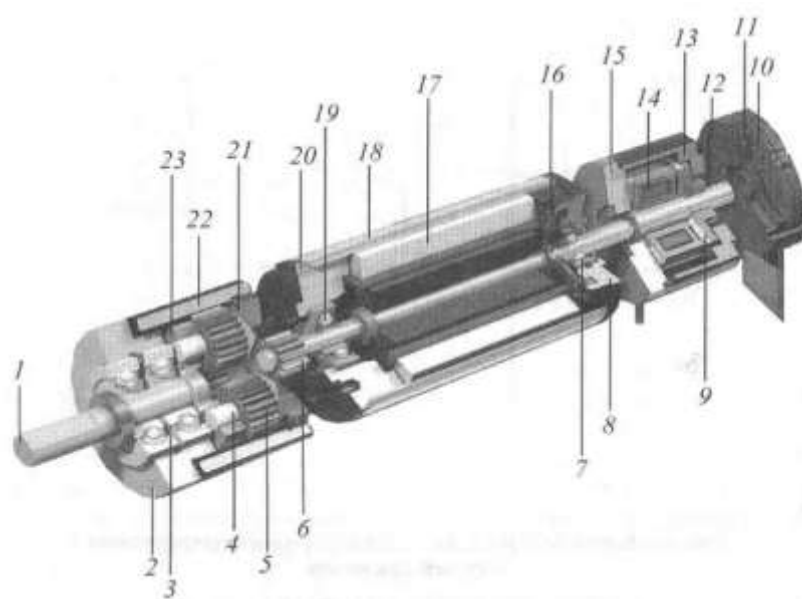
Мехатронний модуль ES-max Махон: 1 – вихідний вал; 2 – фланець редуктора; 3, 7, 19 – підшипники; 4 – вісь; 5 – сателіт планетарної передачі; 6, 21 – зубчасті колеса; 8, 20 – фланець двигуна; 9 – гальмівний диск; 10 – плата керування; 11 – кодовий диск енкадера; 12 – корпус датчика; 13 – корпус гальма; 14 – статор; 15 – кришка; 16 – датчик Хола; 17 – статор електродвигуна; 18 – корпус електродвигуна; 22 – корпус редуктора; 23 – водило
